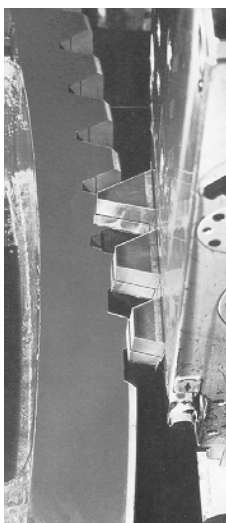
reZ) Schruppen mit Stufenhobelwerkzeug
